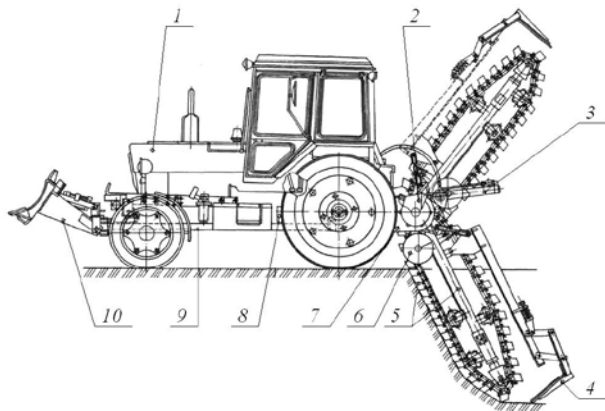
Экскаватор-траншеекопатель ЭТЦ-165А: 1 – трактор базовый; 2 – муфта предельного момента; 3 – гидроцилиндр механизма подъема; 4 – башмак зачистной; 5 – экскаваторное рабочее оборудование; 6 – шнеки; 7 – редуктор привода рабочего органа; 8 – ходоуменьшитель; 9 – рама; 10 – бульдозер универсальный
